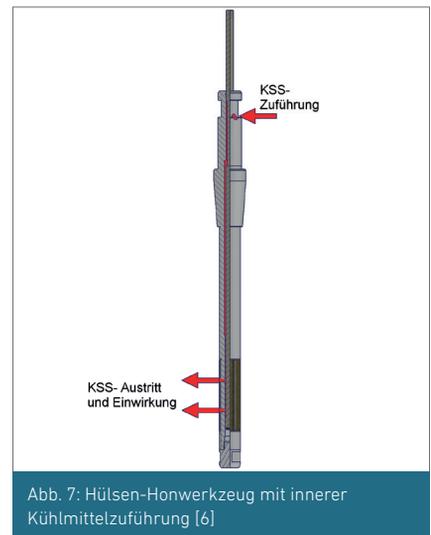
Hülsen-Honwerkzeug mit innerer Kühlmittelzuführung [6]
